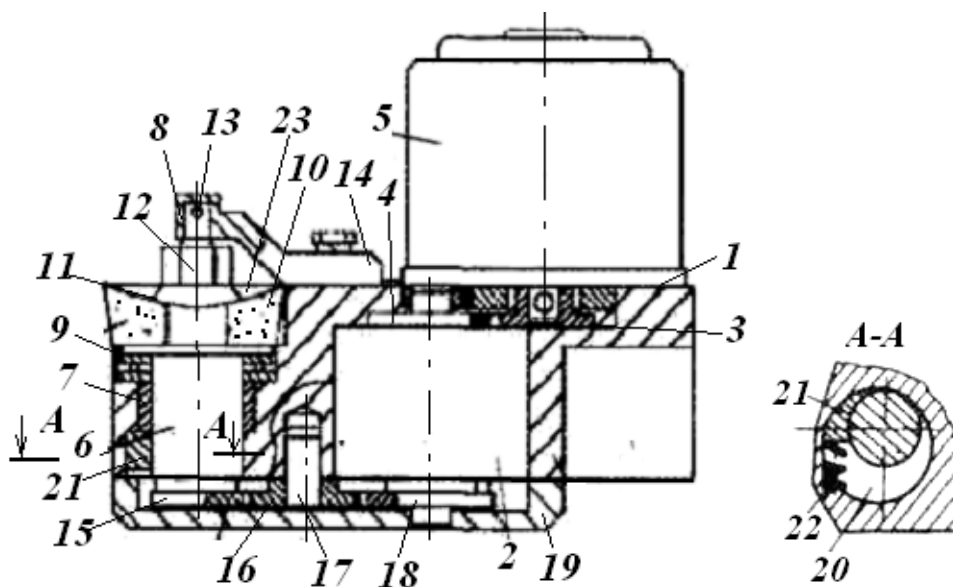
Эскиз резца с непрерывным обновлением режущей кромки для обработки длинномерных стальных валов
